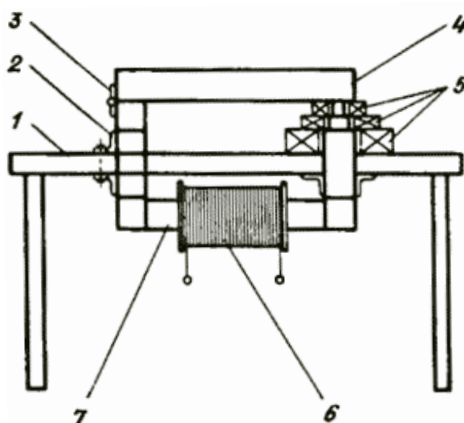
Приспособление для нагрева подшипников индукционным способом:
